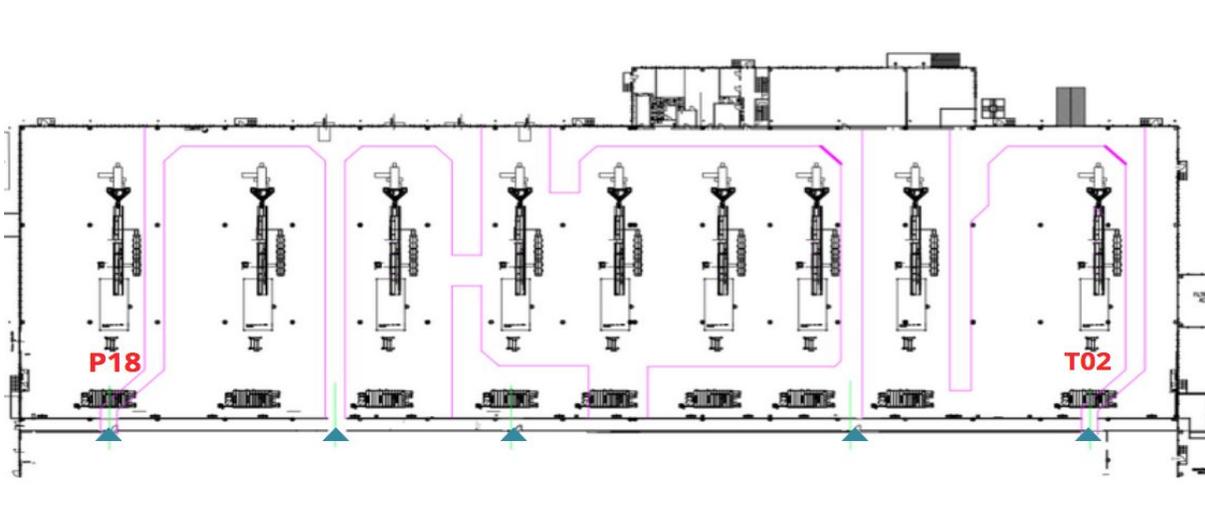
Layout edificio di produzione con in evidenza le linee T02 e P18.
